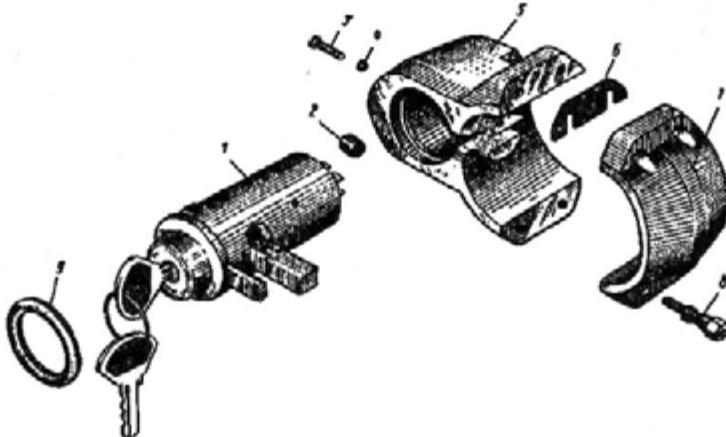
Выключатель (замок) зажигания, выключатель стартера и детали его крепления
